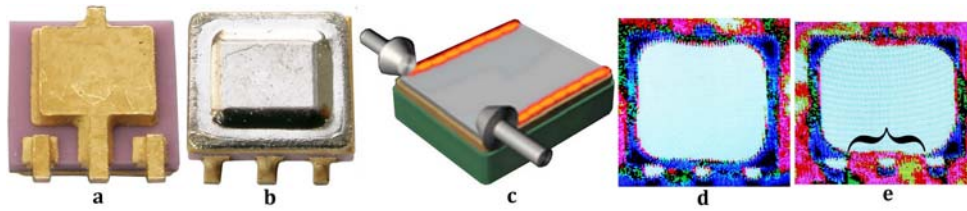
Внешний вид корпуса (а – снизу, b – сверху), схема шовно-роликовой сварки (с), лазерные фотоакустические топограммы герметичного (d) и негерметичного (e) корпусов. Негерметичный участок шва показан фигурной скобкой
